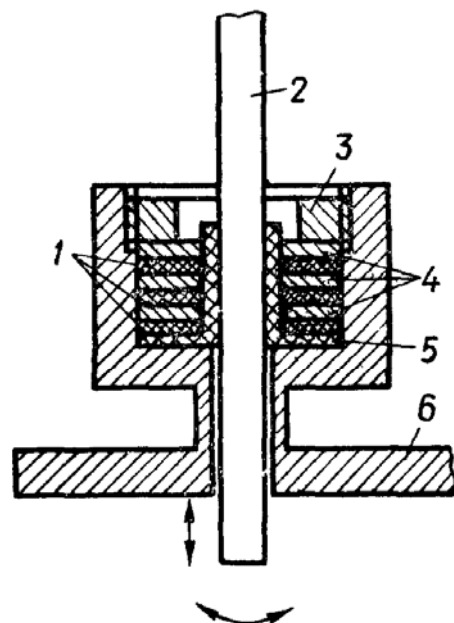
Схема устройства для передачи вращательного или поступательного движения в вакуумную полость:
